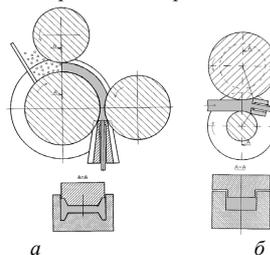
Устройства для получения профилей и проволоки из цветных металлов и сплавов: а – из порошковых материалов; б – из литой заготовки
